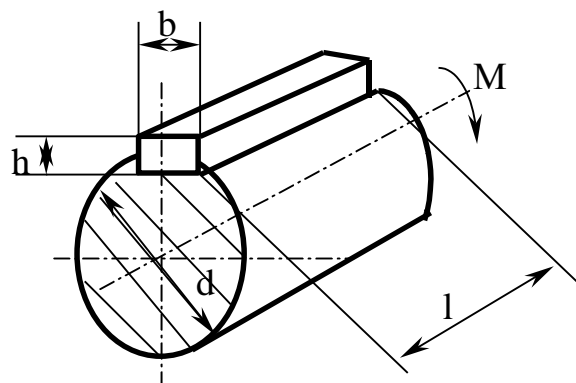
Розрахункова схема шпонкового з'єднання.
